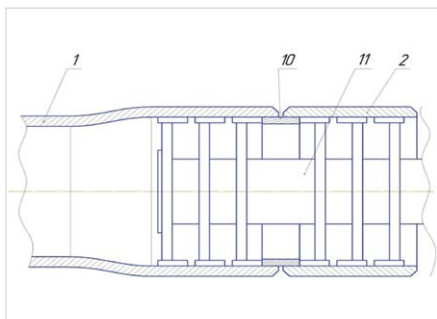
Сборка трубы и втулки перед сваркой с помощью центриатора
